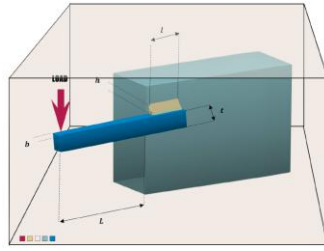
Сварка балки с параметрами толщина сварного шва, длина, высота и толщина присоединяемой части стержня
